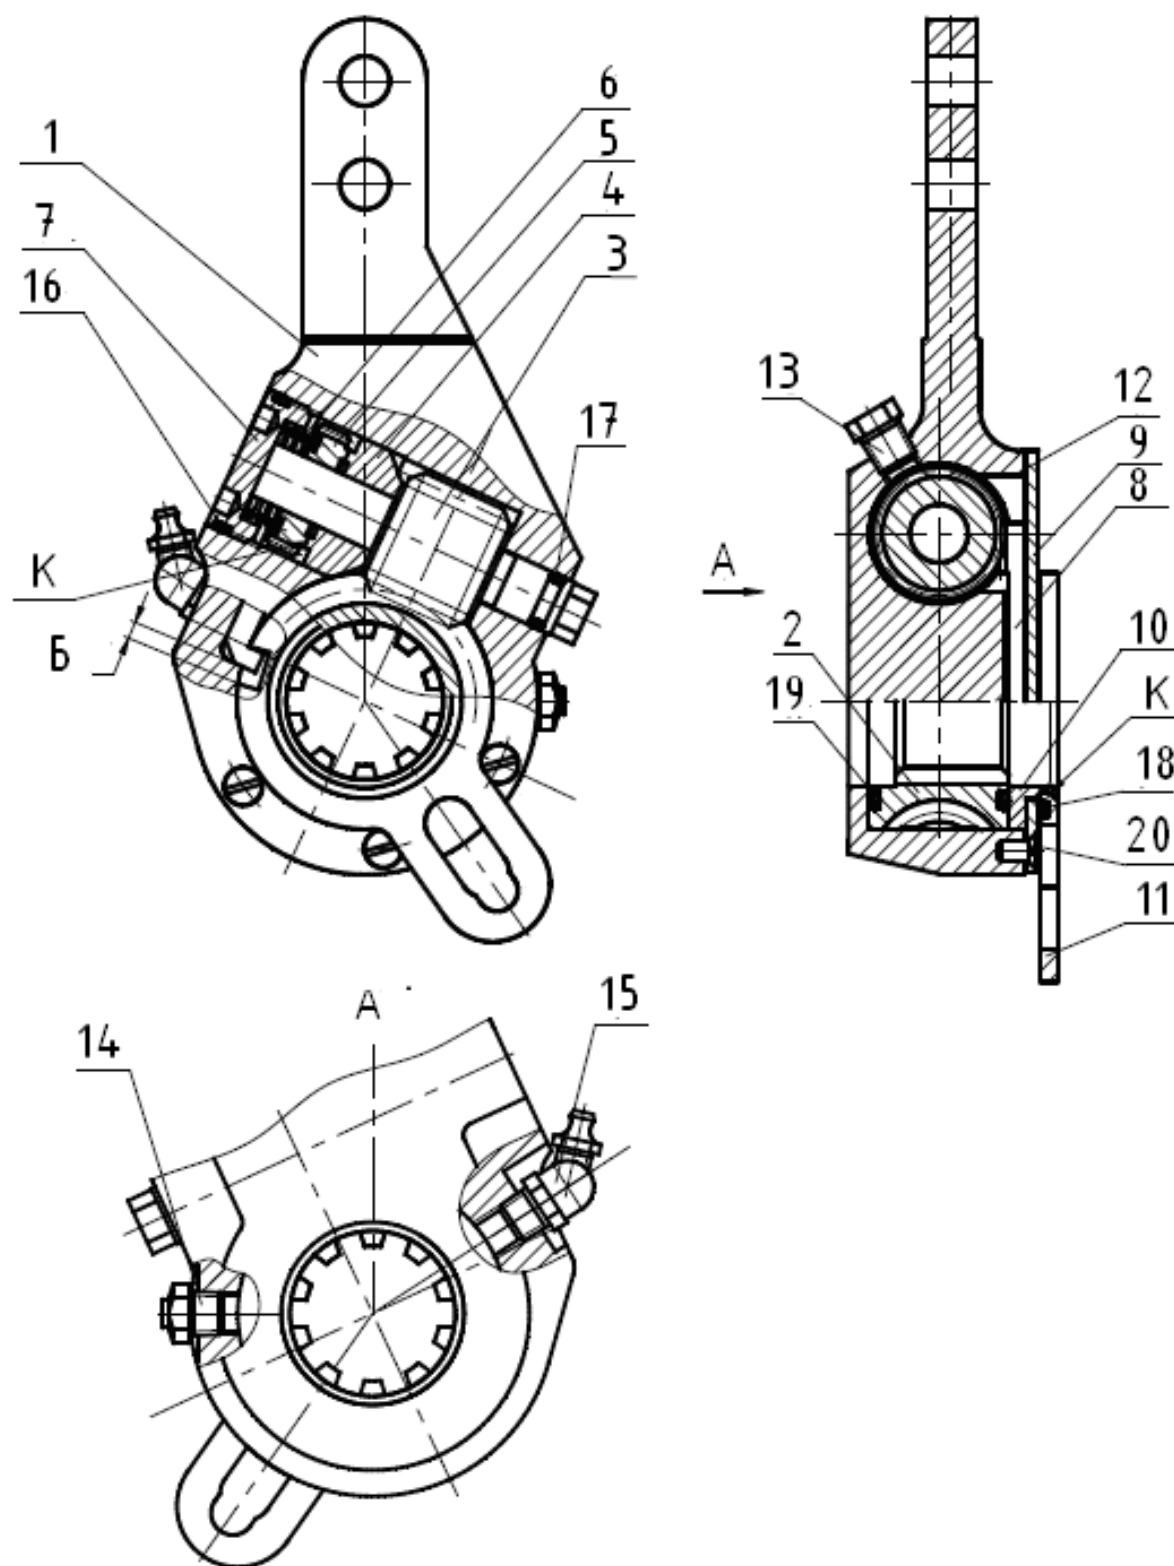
Устройство автоматического регулятора зазора тормозных колодок автомобилей семейства МАЗ: 1 – корпус; 2 – шестерня; 3 – вал червячный; 4 – неподвижная полумуфта; 5 – подвижная полумуфта; 6 – пружина; 7 – заглушка; 8 – толкатель; 9 – крышка; 10 – кольцо управляющее; 11 – поводок; 12 – прокладка; 13 – пробка; 14 – предохранительный клапан; 15 – масленка; 16, 17, 18, 19 – кольца; 20 – винт
